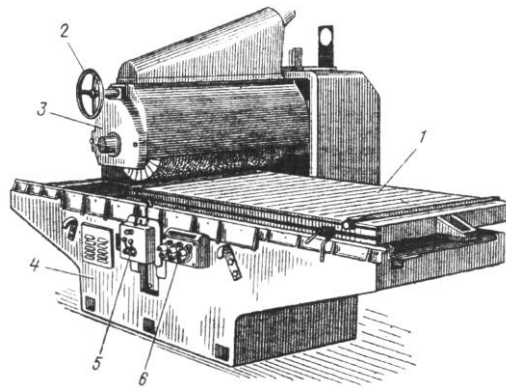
Полірувальний однобарабанний верстат ПІБ: 1 - каретка; 2 - механізм піднімання супорта; 3 - супорт; 4 - станина; 5 - гідропанель; 6 - пульт керування
